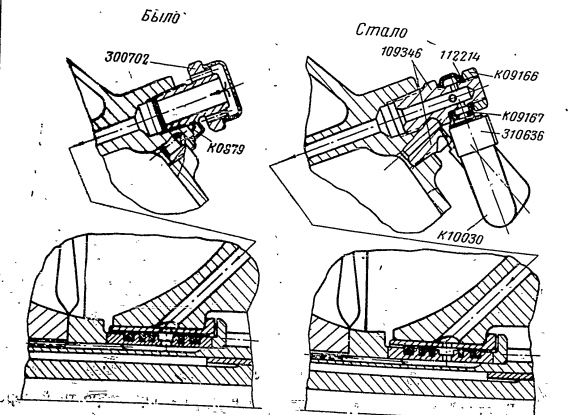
Крышка сателлитов валика редуктора двухскоростной передачи нагнетателя.
